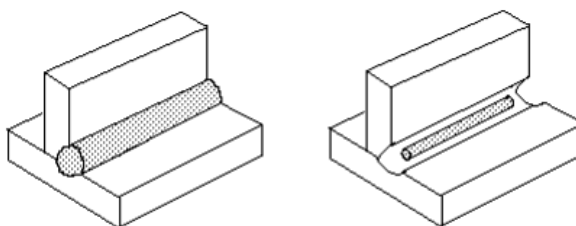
Defecto de esfuerzos residuales en piezas soldadas⁷⁵
